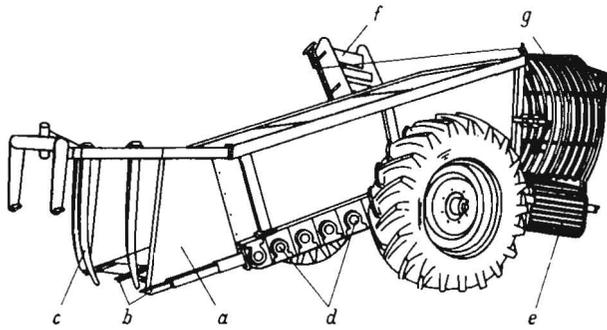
Steinsammelmaschine für Bodenschichten bis zu 30 cm Tiefe
